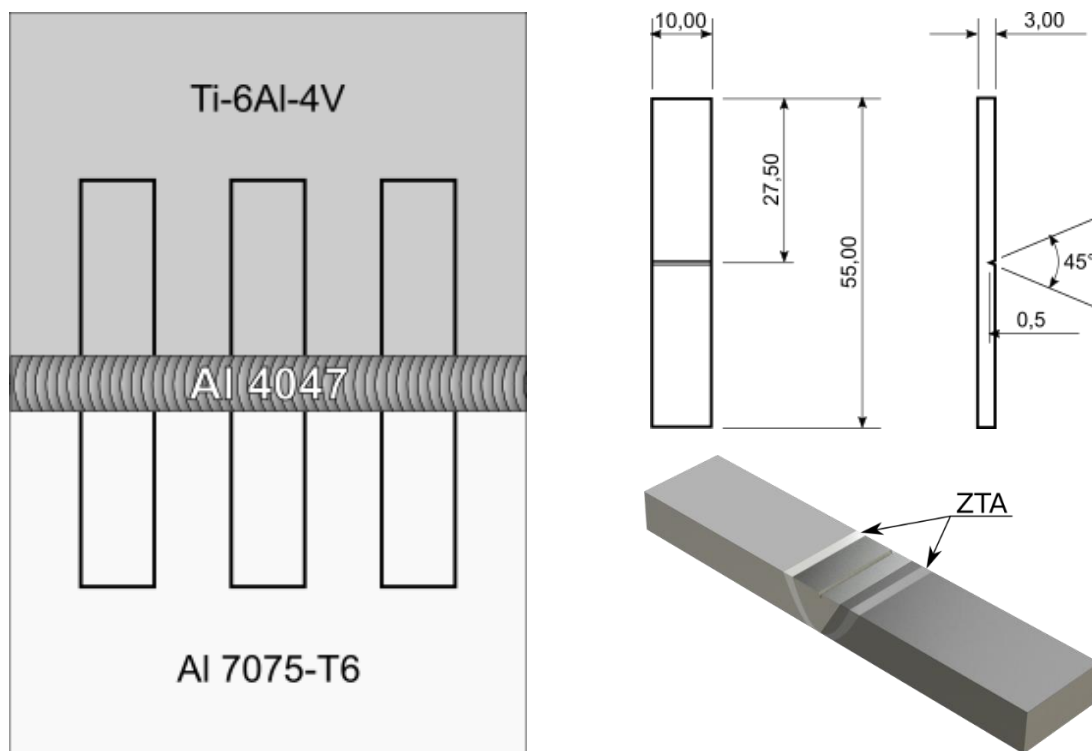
Desenho representativo da forma de obtenção dos corpos de prova e suas dimensões para ensaio de impacto (Charpy).
